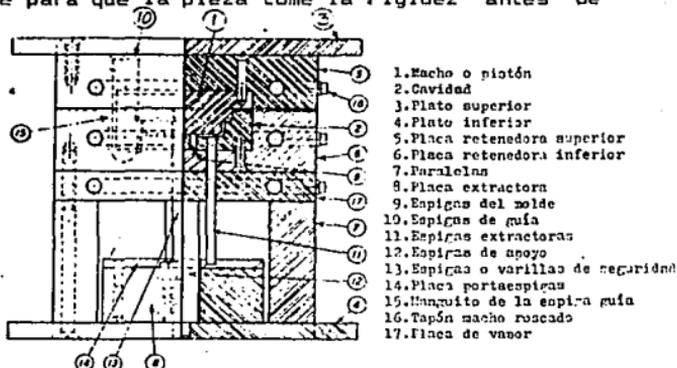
Molde de compresión con macho de asiento mostrando detalles de la construcción del molde y los nombres de las partes del molde.
